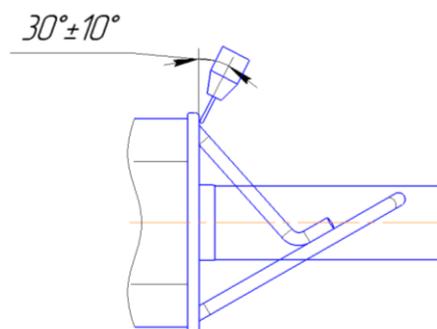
Сварка основного глушителя и кронштейна
